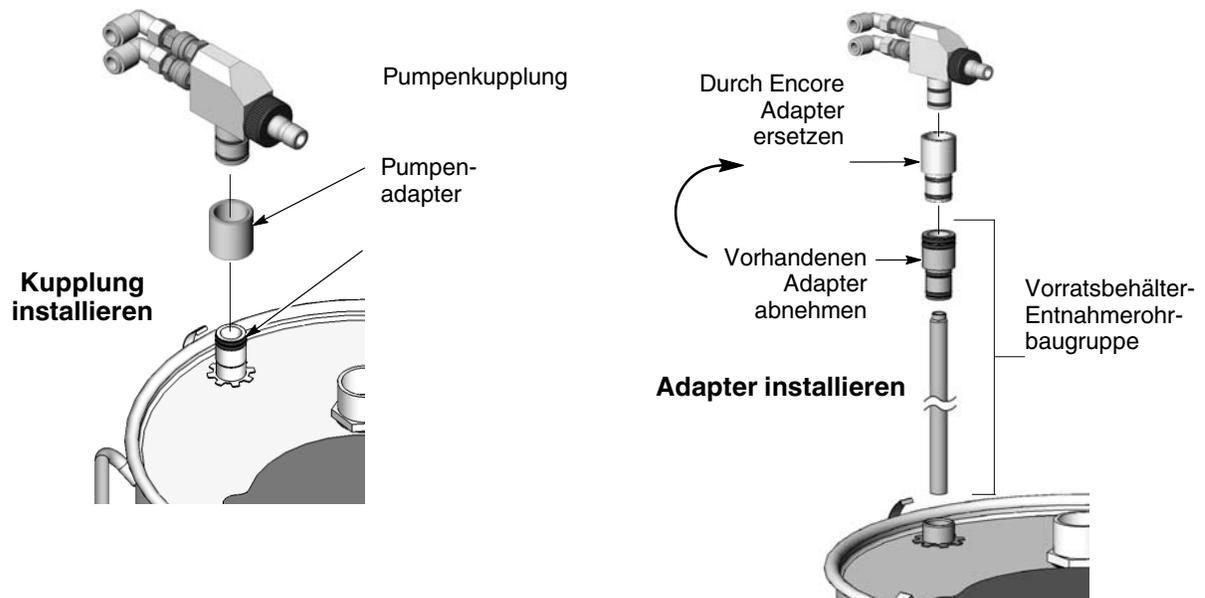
Pumpe mit Adaptersatz oder Kupplung auf Vorratsbehältern HR oder NHR installieren
